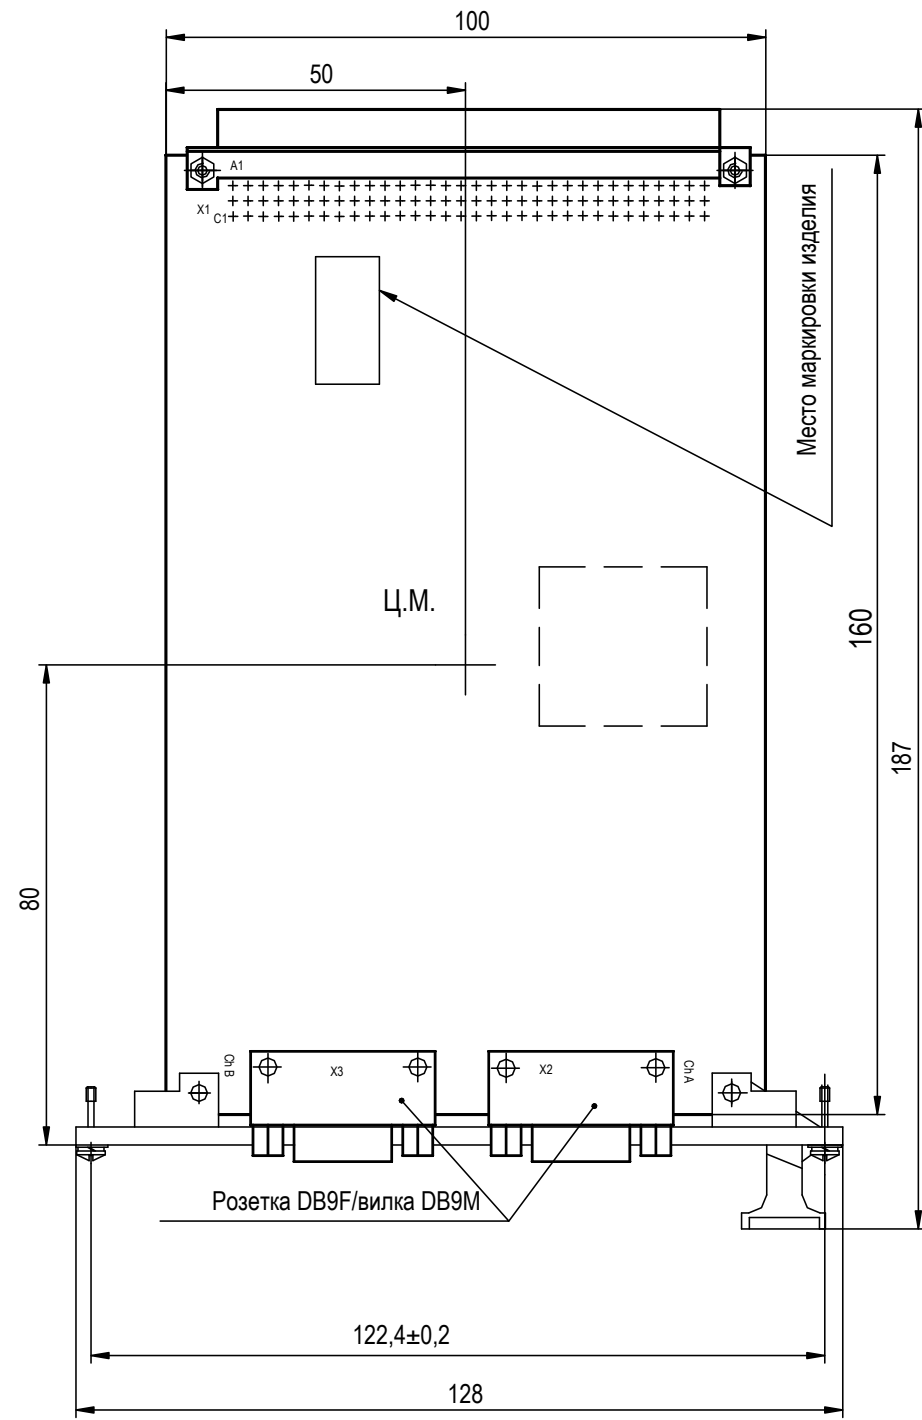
а – Внешний вид и габаритные размеры изделия с соединителем DB9
